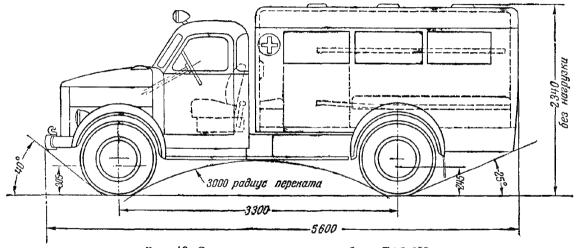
Схема санитарного автомобиля ПАЗ-653.
